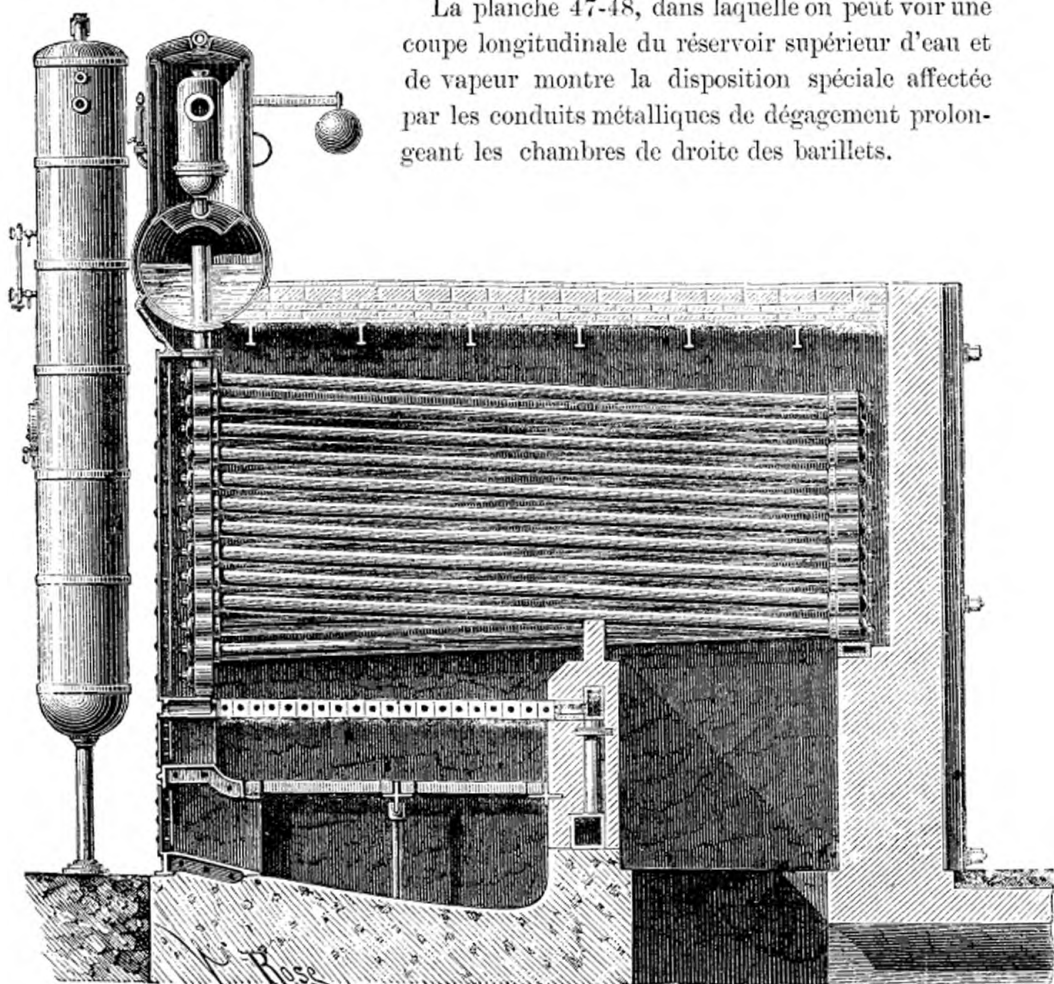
GÉNÉRATEUR LENCAUCHEZ, COUPE LONGITUDINALE
